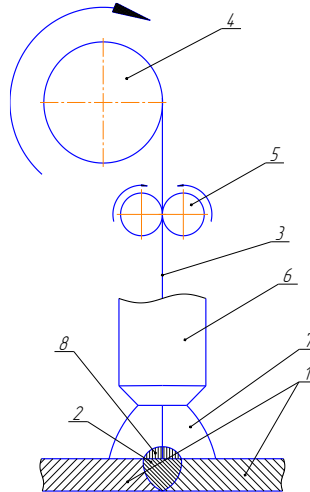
Схема напівавтоматичного зварювання у захисній суміші
